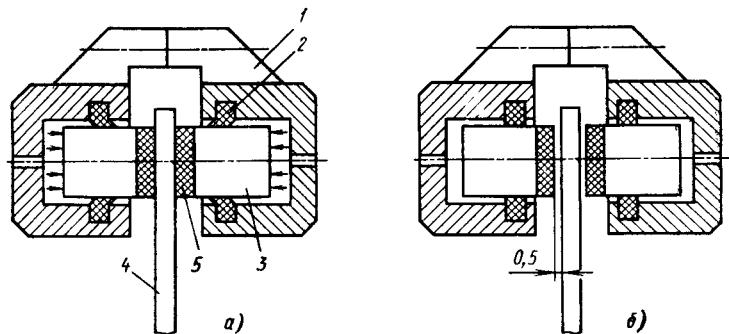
Схема двухпоршневой скобы дискового тормоза:
